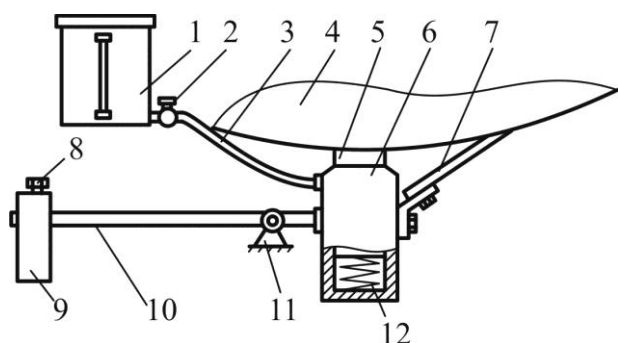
Устройство для очистки рабочей поверхности верхнего шкива ленточнопильного станка:
